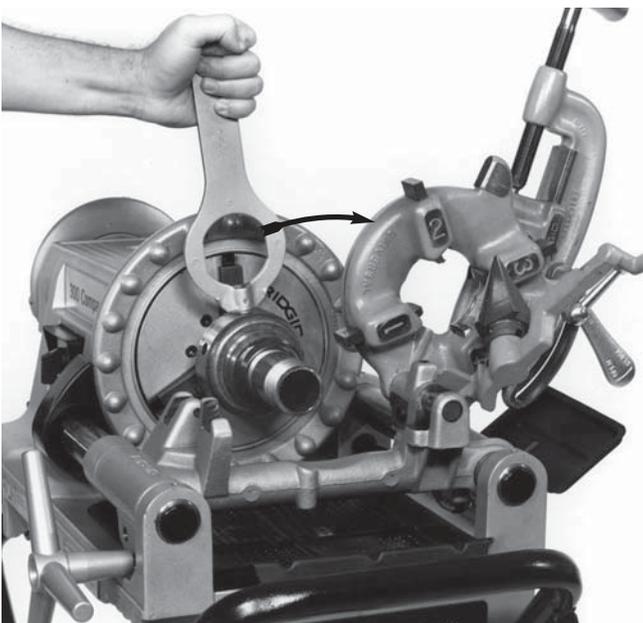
Установка необработанного патрубка и освобождение готового патрубка с помощью ключа
